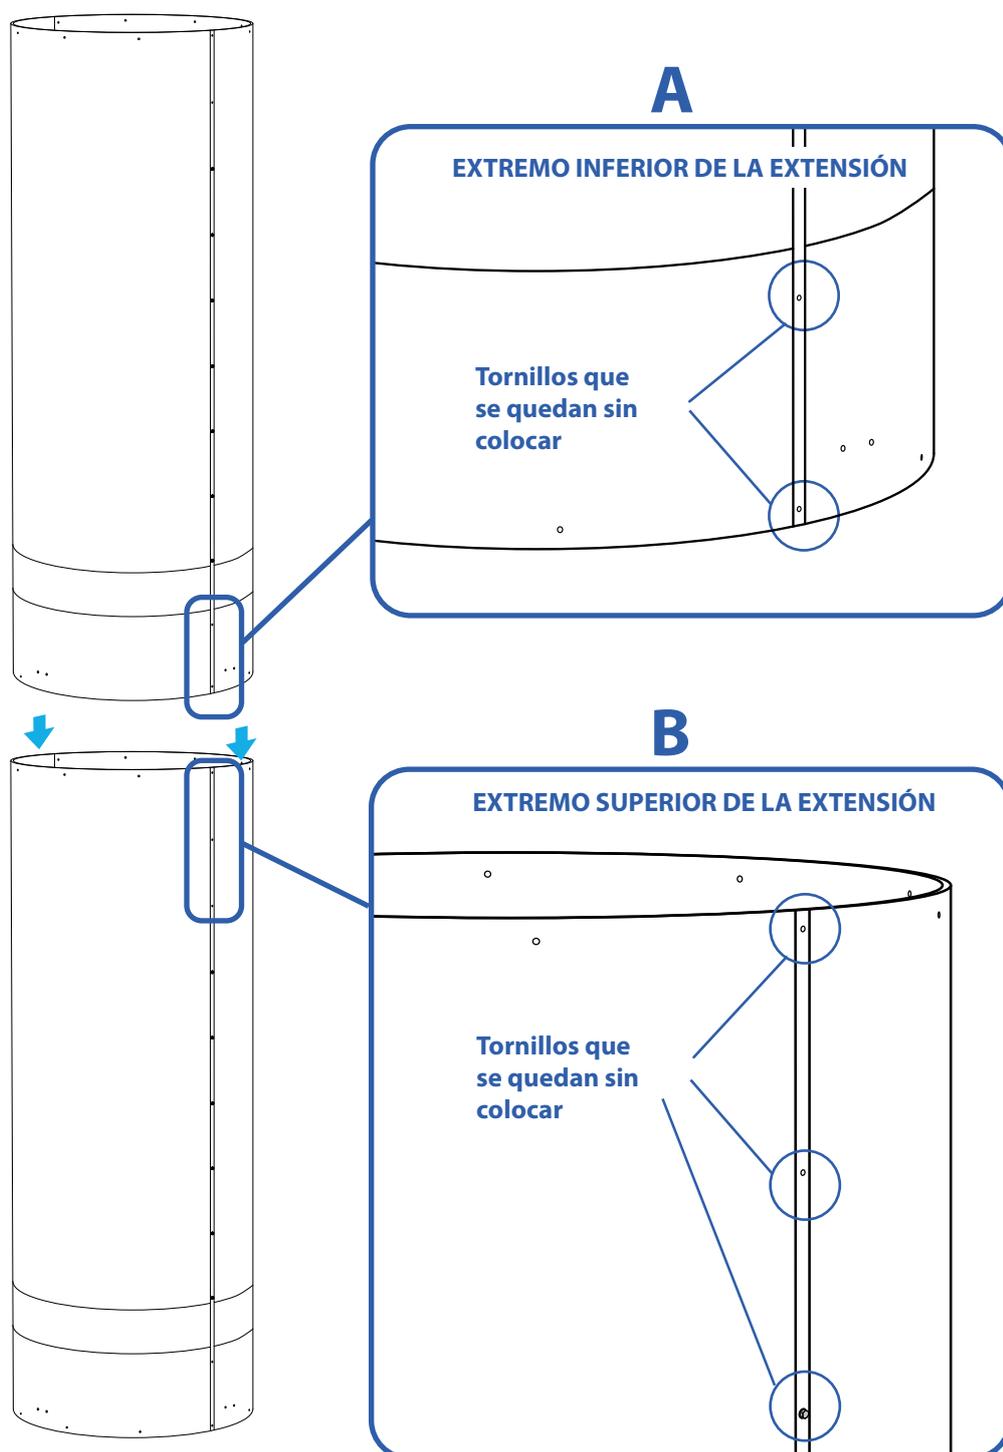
Esquema de tornillos que se quedan sin colocar.
